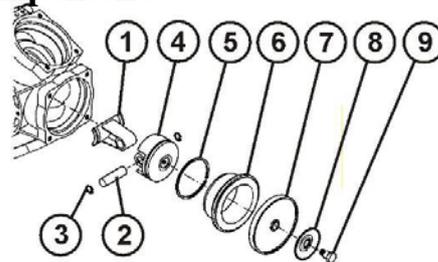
/1 Beschreibung der Pumpe - Zylinder
